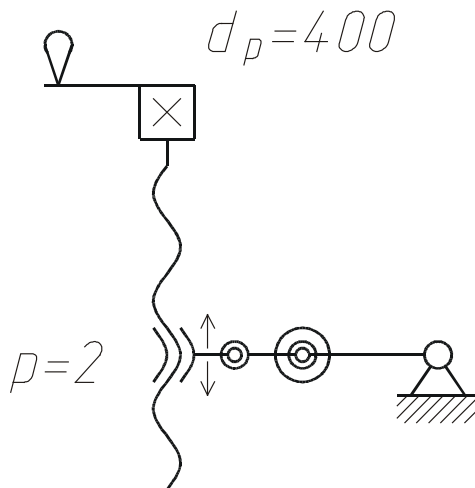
Кінематична схема натягувального устрою транспортера печі ФТЛ2-66
